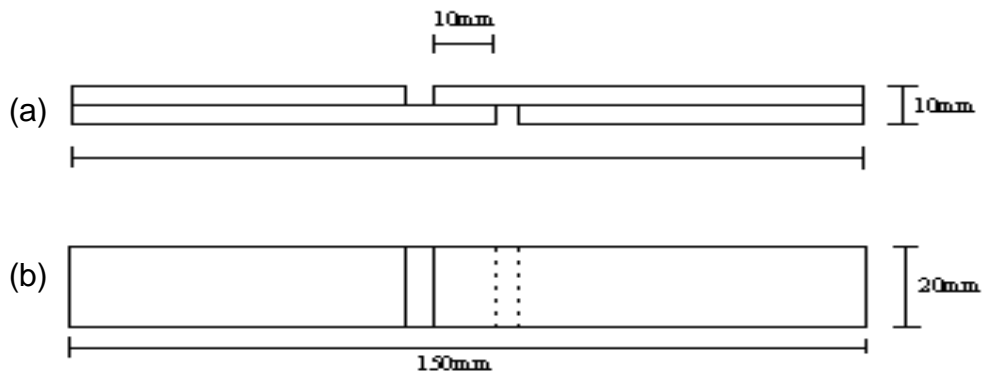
DESENHO ESQUEMÁTICO DO CORPO-DE-PROVA: (a) VISTA LATERAL E (b) VISTA SUPERIOR
